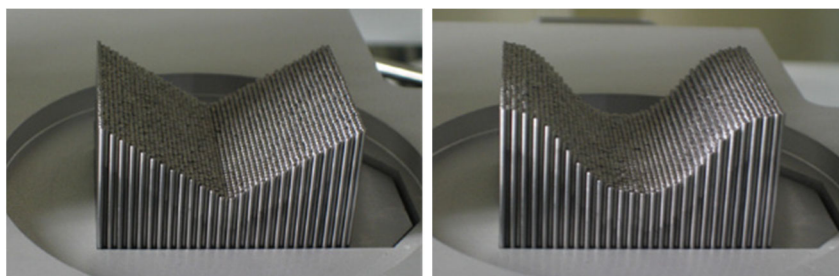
Superfícies geradas pelo sistema FlexiMoldt
